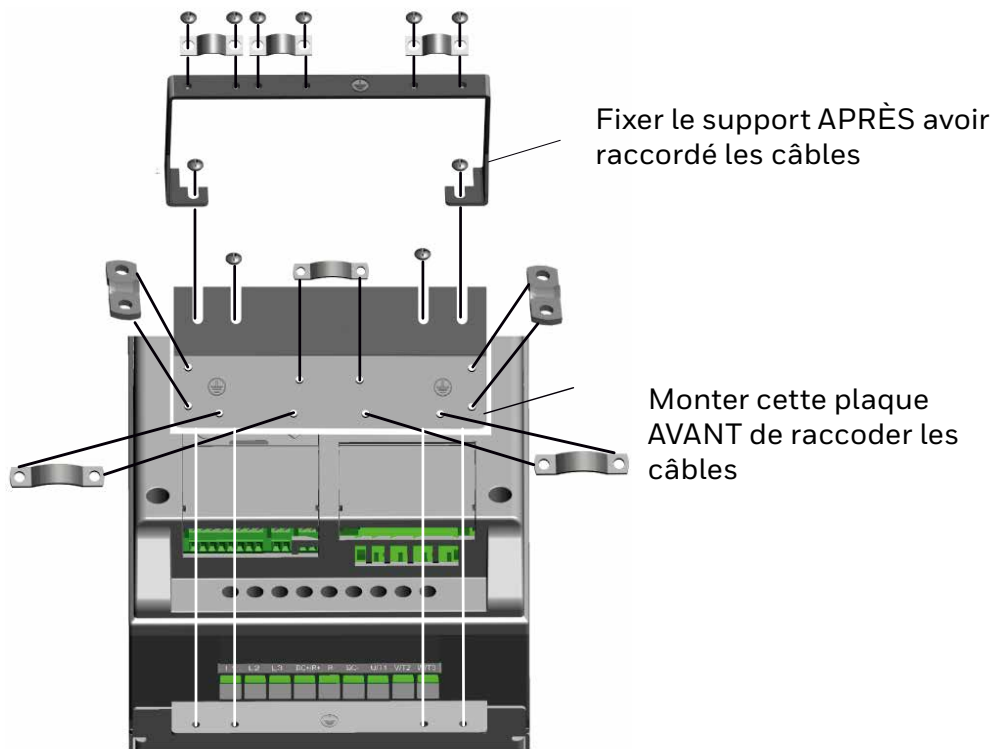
Montage de la plaque PE et du support de câble API, MI4 - MI5
